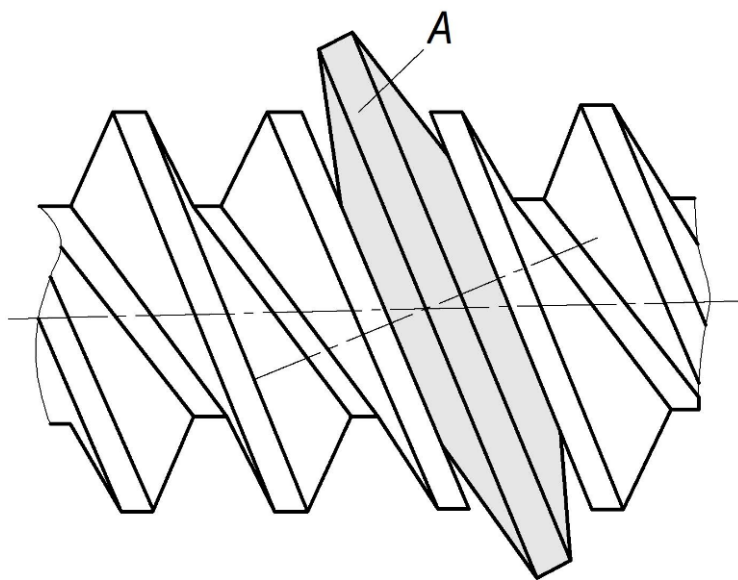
Нарізування черв'яка дисковою фрезою
